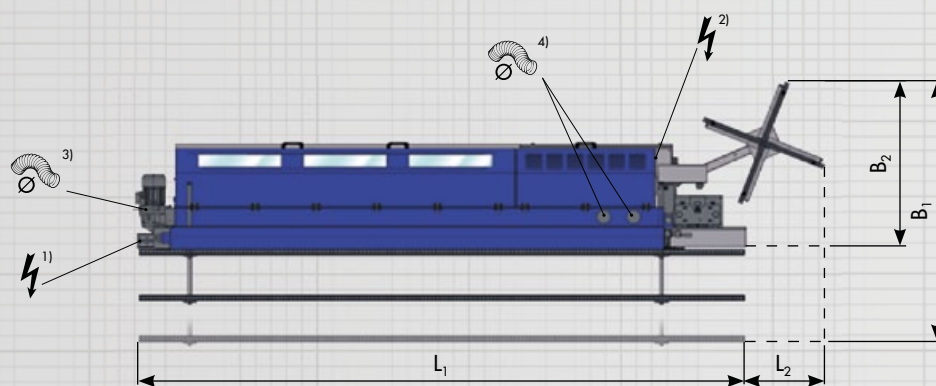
Photo symboles G 220, G 330, G 360, G 380, G 480, G 500
